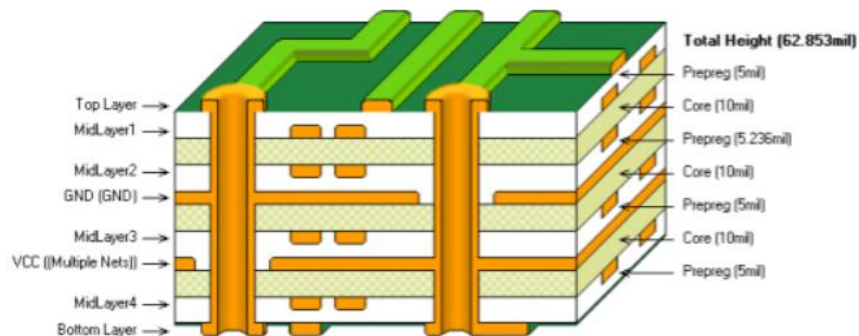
Esquema de uma placa PCB obtida através de multicamada. [2]
